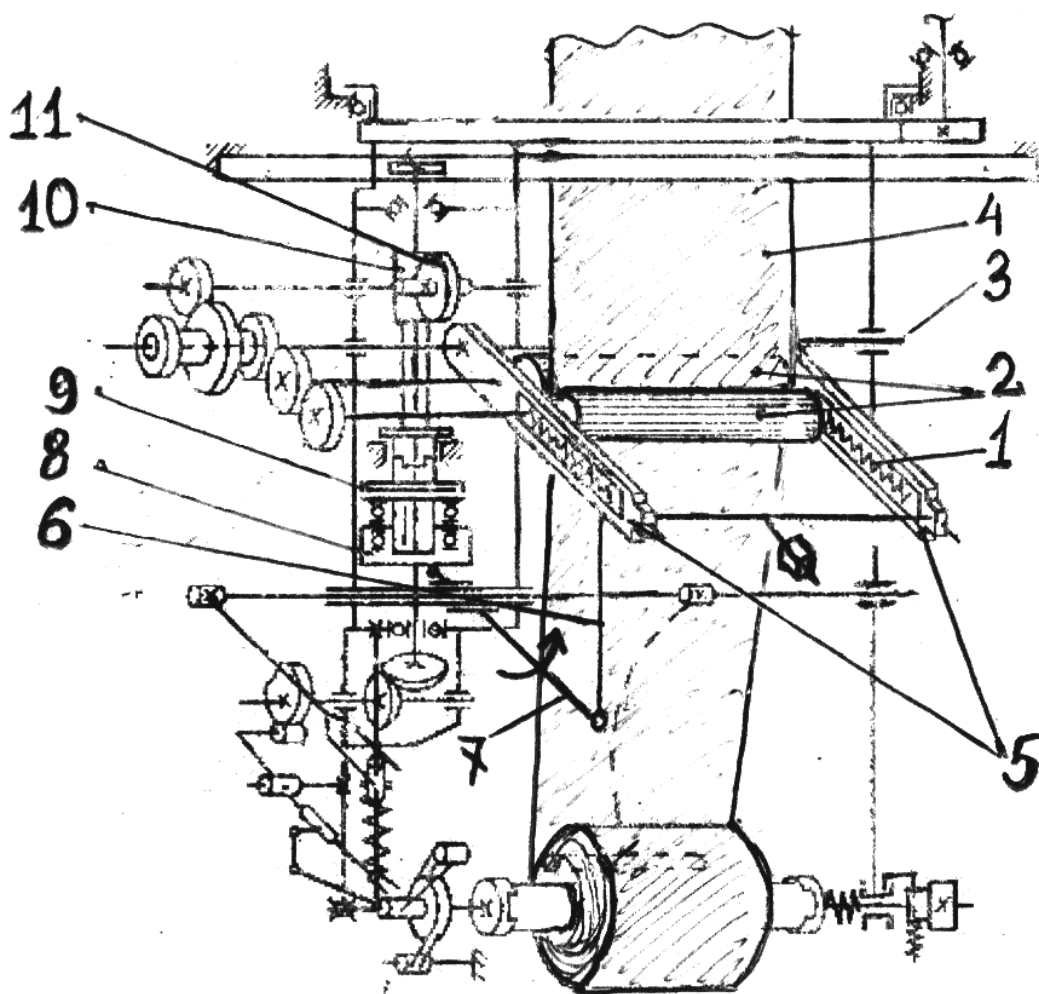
Кинематическая схема механизма оттяжки и накатки полотна машины типа МС:
